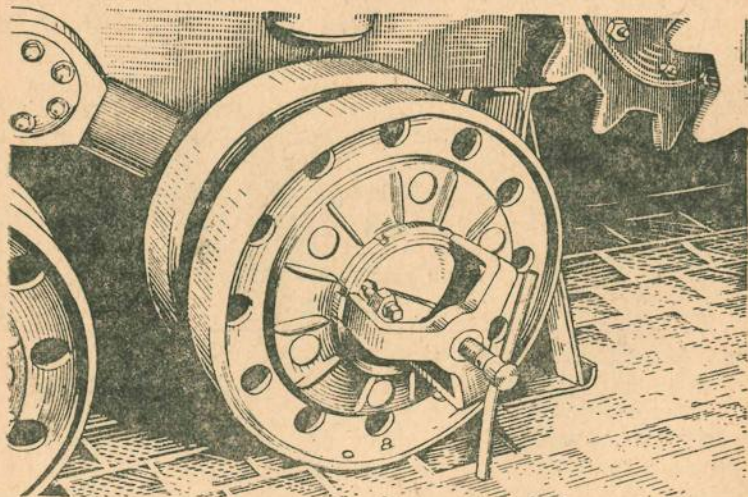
Выпрессовка крышки нижнего катка при помощи приспособления
